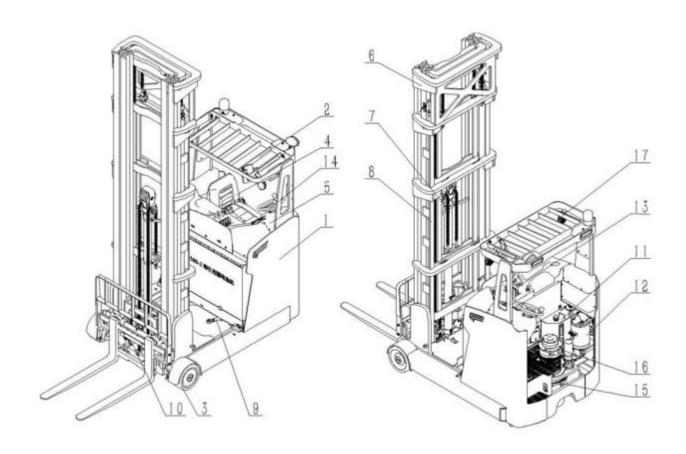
Конструкция ричтрака. Сборочный чертеж:
